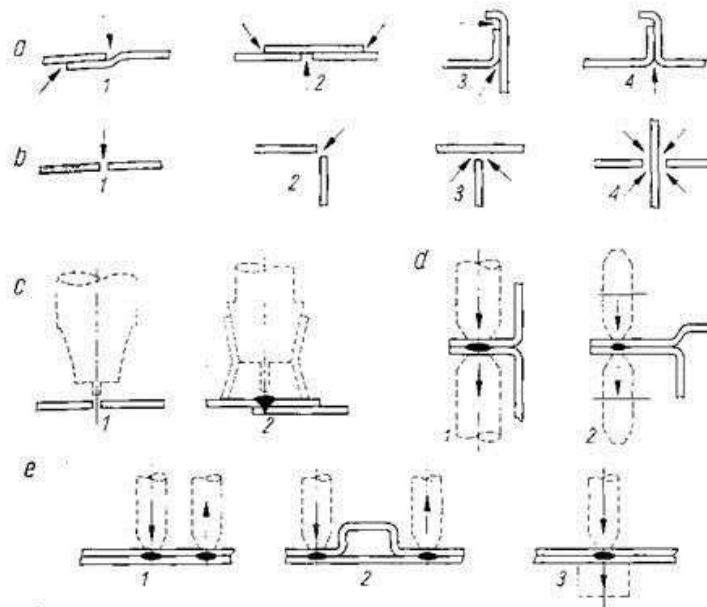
Нероз'ємні з'єднання кузовних деталей, що виконуються зварювання.
